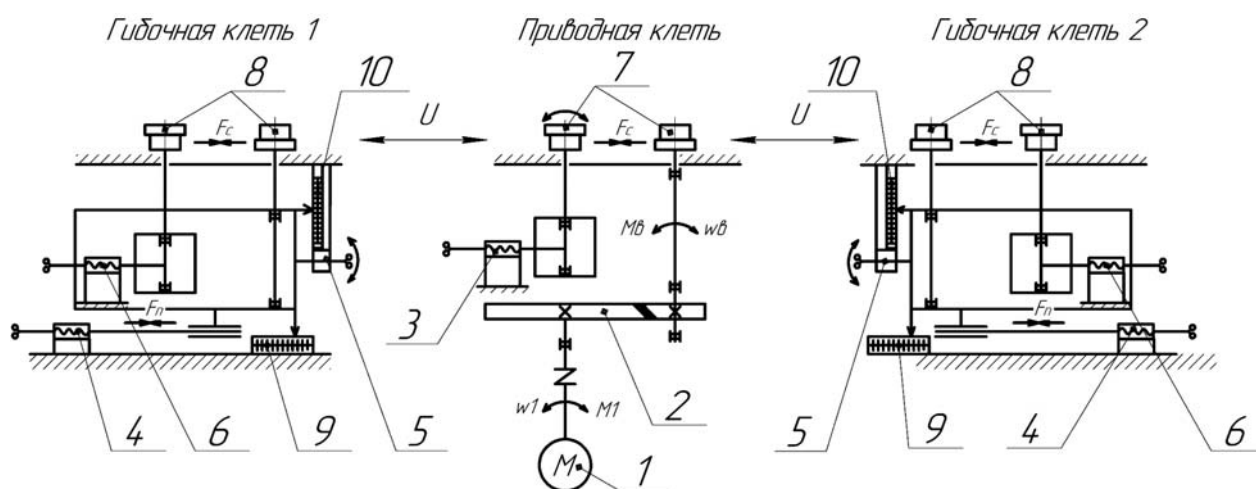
Кинематическая схема установки правильно-гибочной роликовой
